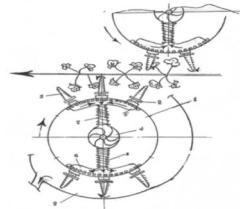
Вид сверху на принцип работы хлопкоуборочной машины с горизонтальным шпинделем
